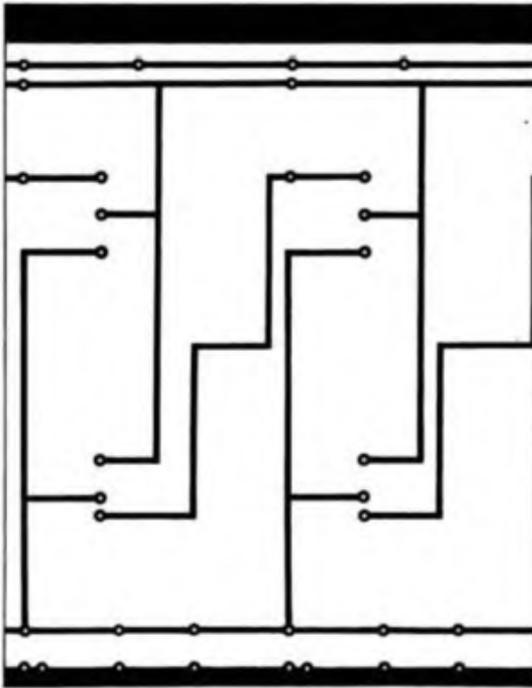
Layout der Bestückungsseite der Ansteuerplatine
